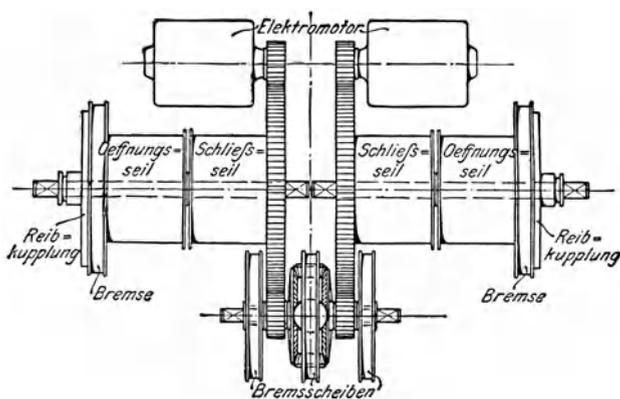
Greiferwinde mit Kegelräderwendegetriebe auf der Vorgelegewelle.
